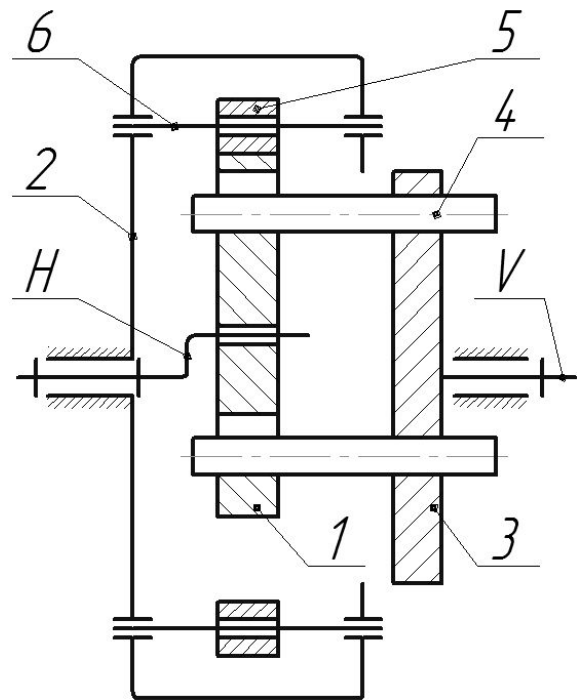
Планетарно-цевочный редуктор схемы К-Н-V.
